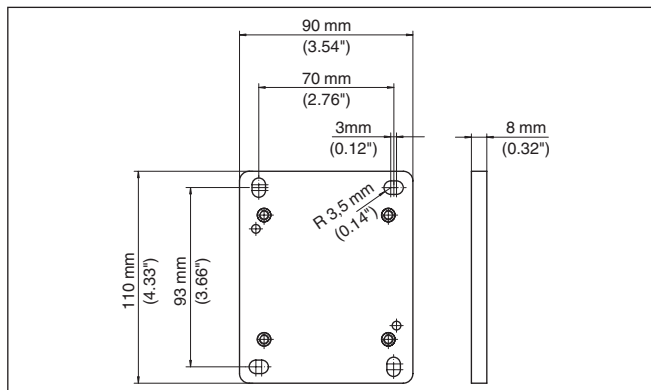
Схема отверстий - планка для настенного монтажа (выносной корпус)
